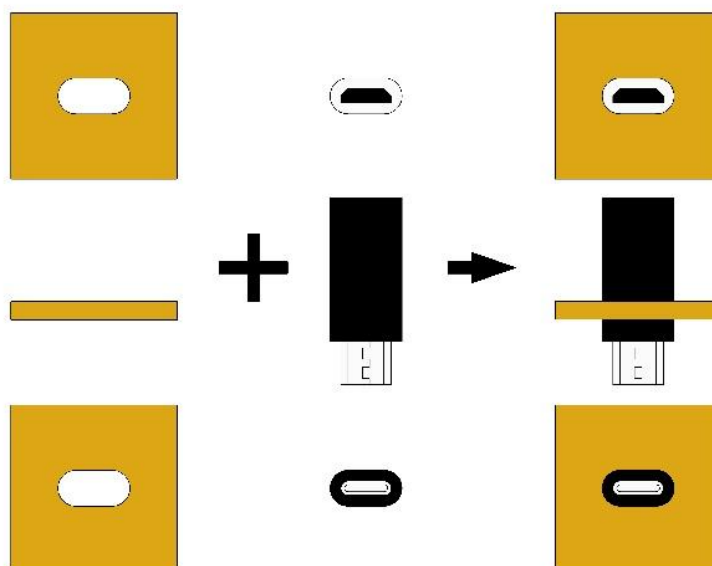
Preparación de la pila 1. Vista inferior, planta y alzado
